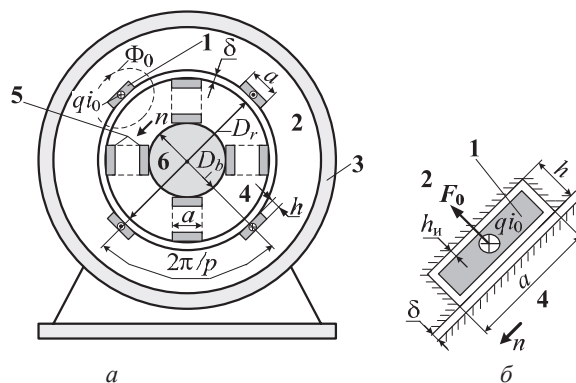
Бесконтактный импульсный компрессионный генератор: 1) обмотка статора; 2) ферромагнитный шихтованный статор; 3) корпус статора; 4) ферромагнитный шихтованный ротор; 5) короткозамкнутые обмотки ротора; б) вал; а — ширина пазов обмоток статора и ротора; h — глубина паза обмотки статора; δ — воздушный зазор между ротором и статором; D_r , D_b — диаметры ротора и вала соответственно; p — число пар полюсов; n — число оборотов ротора в минуту; i_0 — ток в обмотке статора в момент максимума индуктивности; q — число последовательных проводников с током i_0 в пазу обмотки статора; Φ_0 — магнитный поток пары полюсов обмотки статора в момент максимума индуктивности; h_n — толщина изоляции обмотки статора; F_0 — сила, действующая на обмотку статора в момент максимума индуктивности
